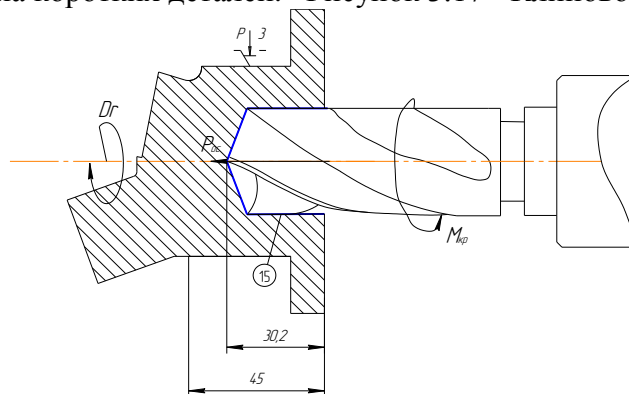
Схема рассверливания отверстия детали «Крышка».
